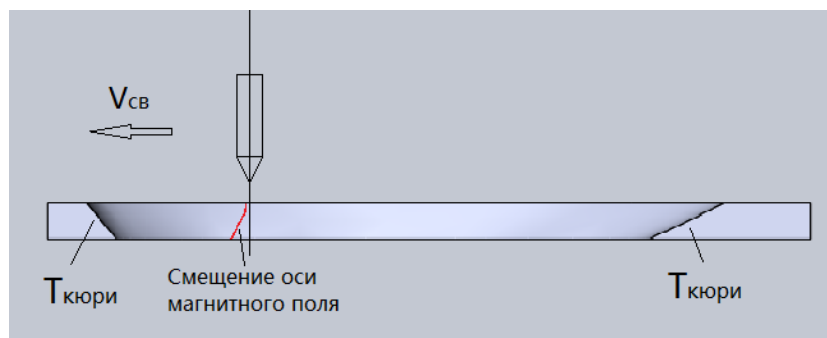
Смещение оси магнитного поля при дуговой сварке магнитных металлов [Displacement of the axis of the magnetic field during arc welding of magnetic metals]
